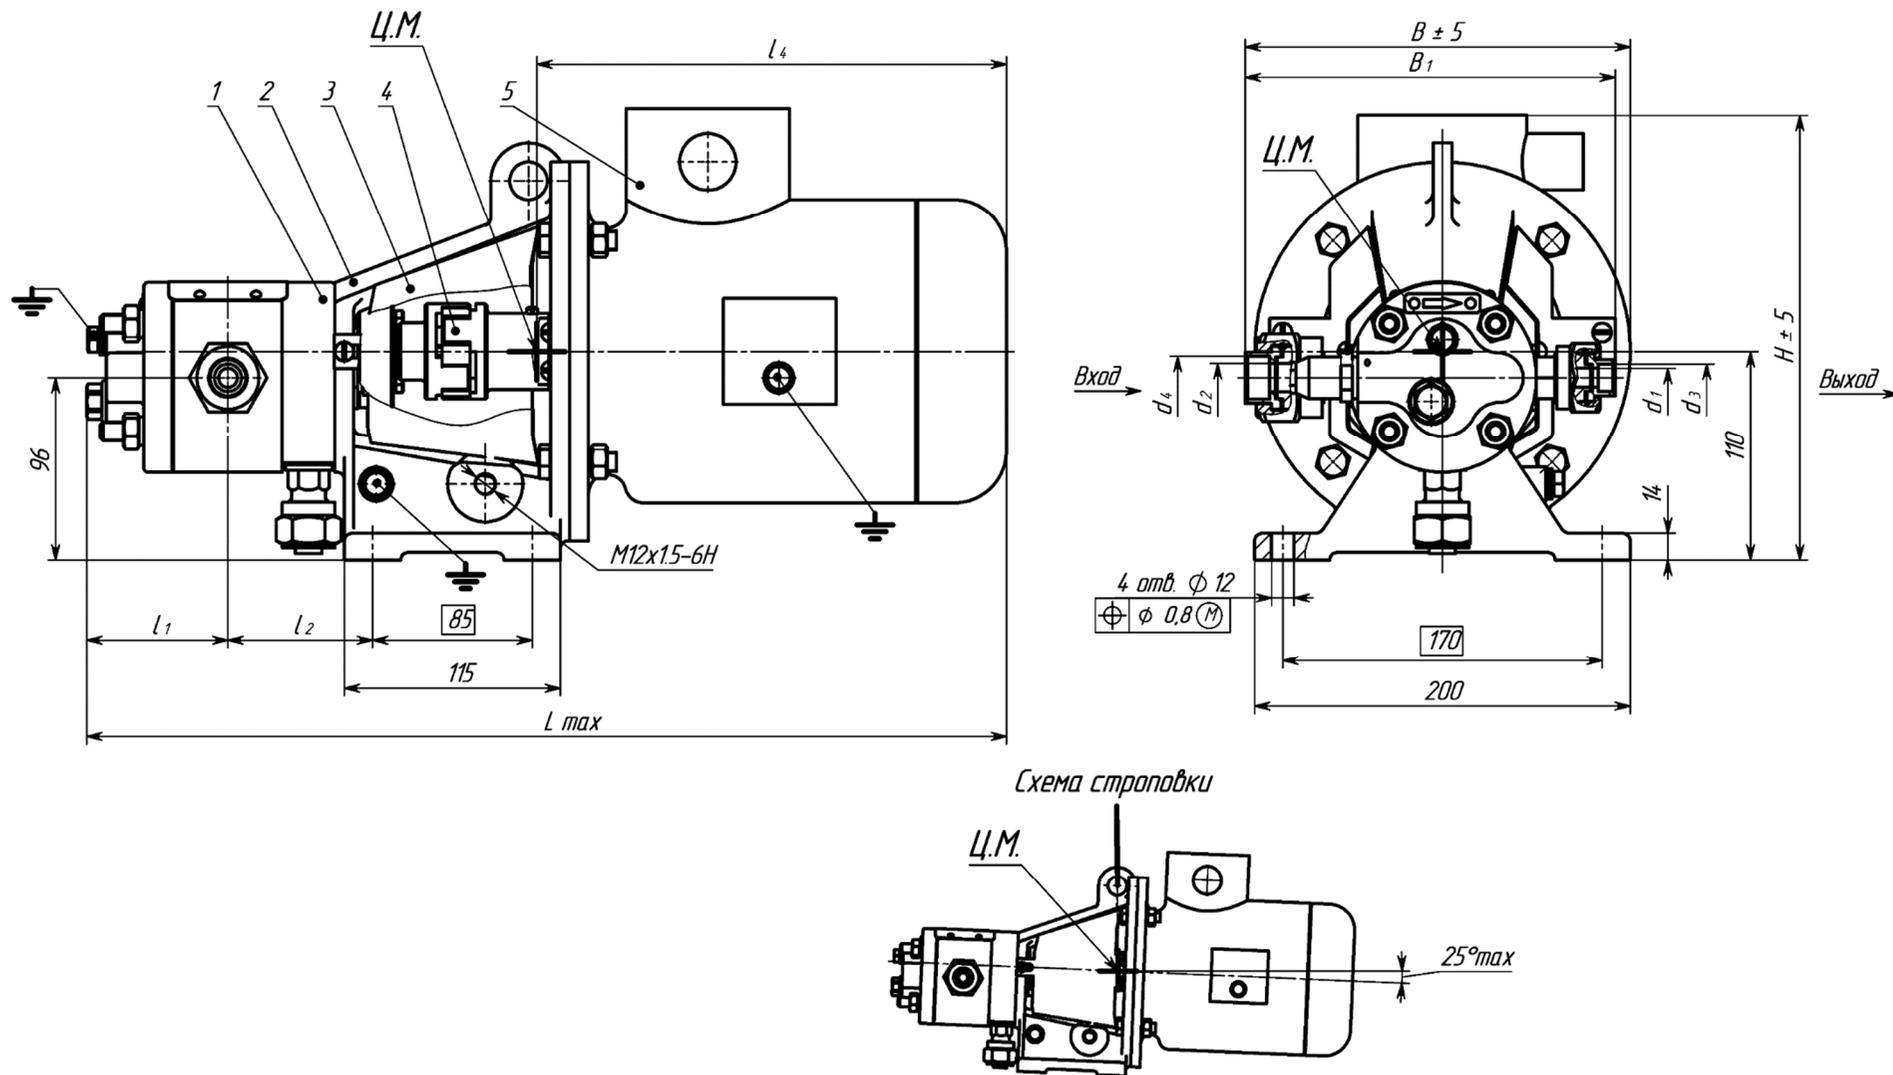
Габаритный чертеж агрегата типа НМШФ с левым вращением ведущего ротора
